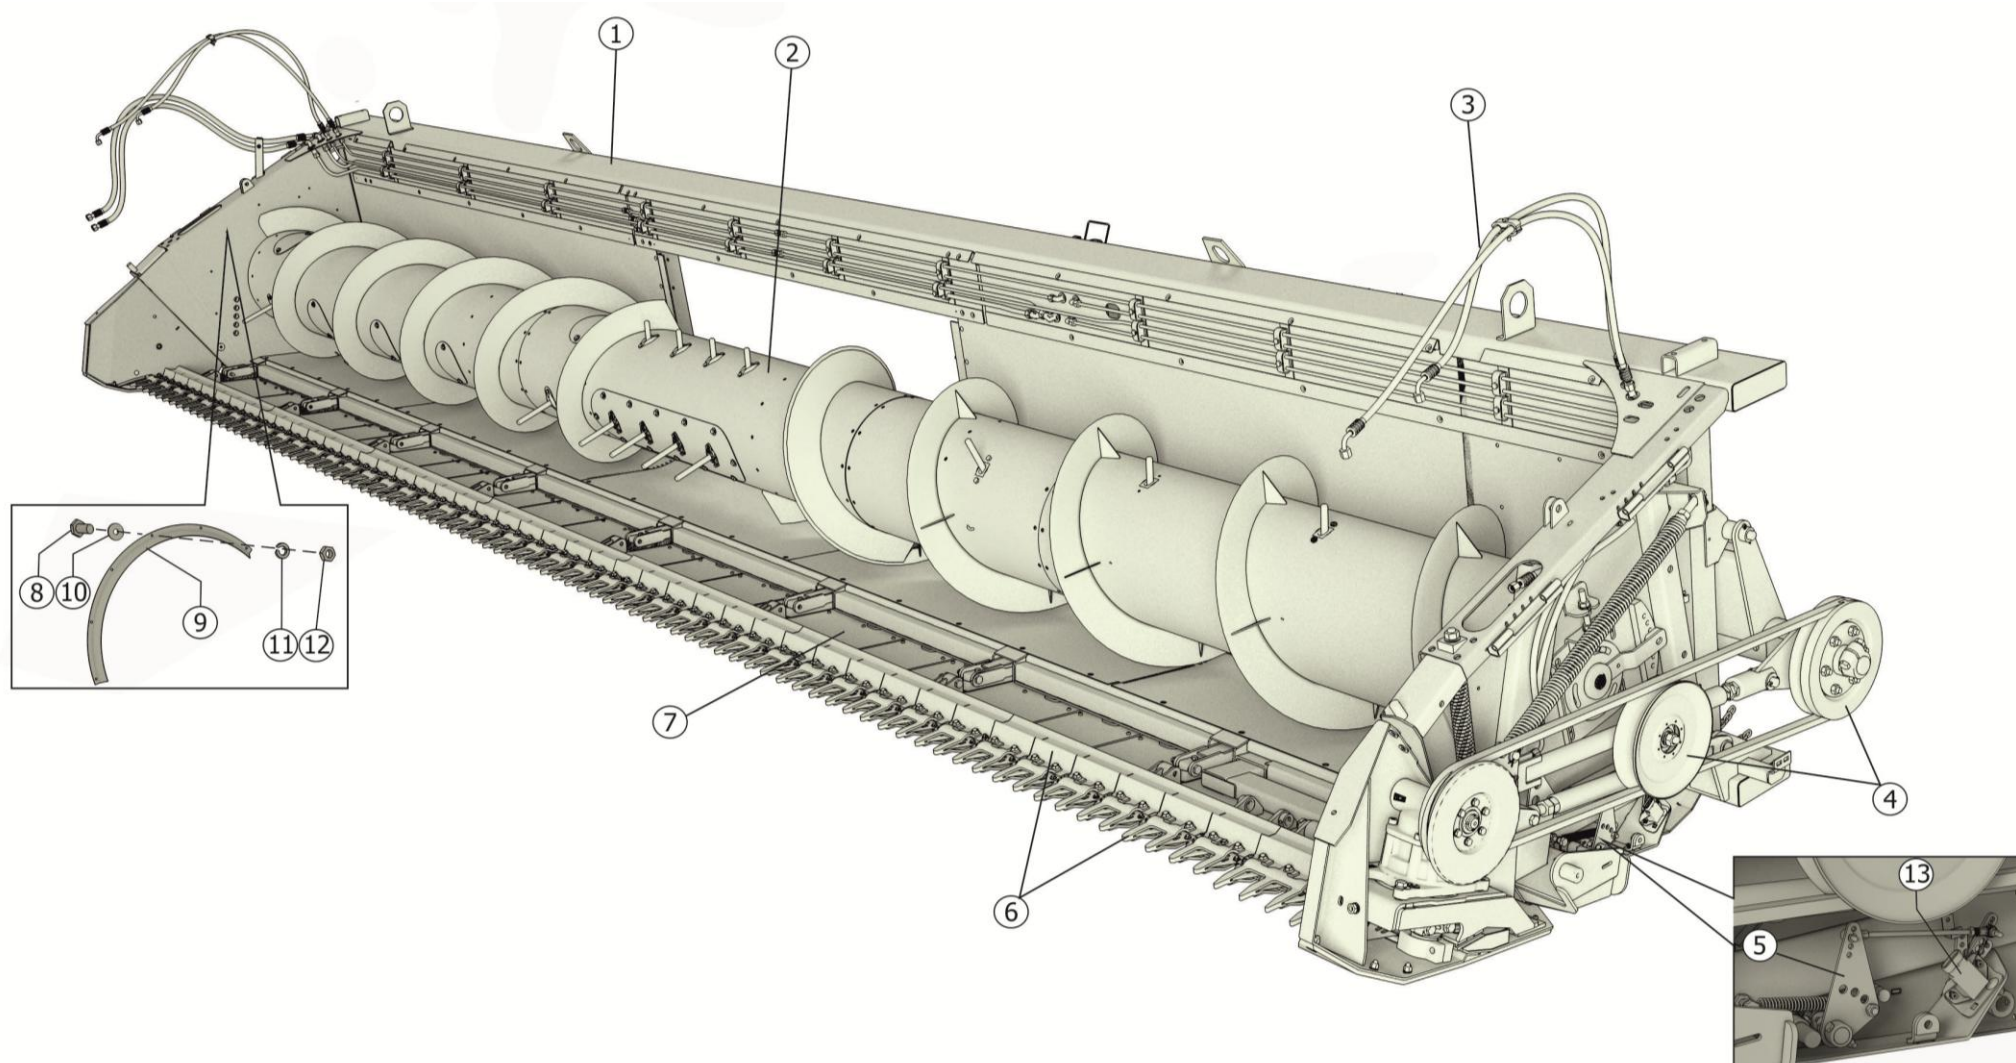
Корпус ЖСУ-704.01.00.000
